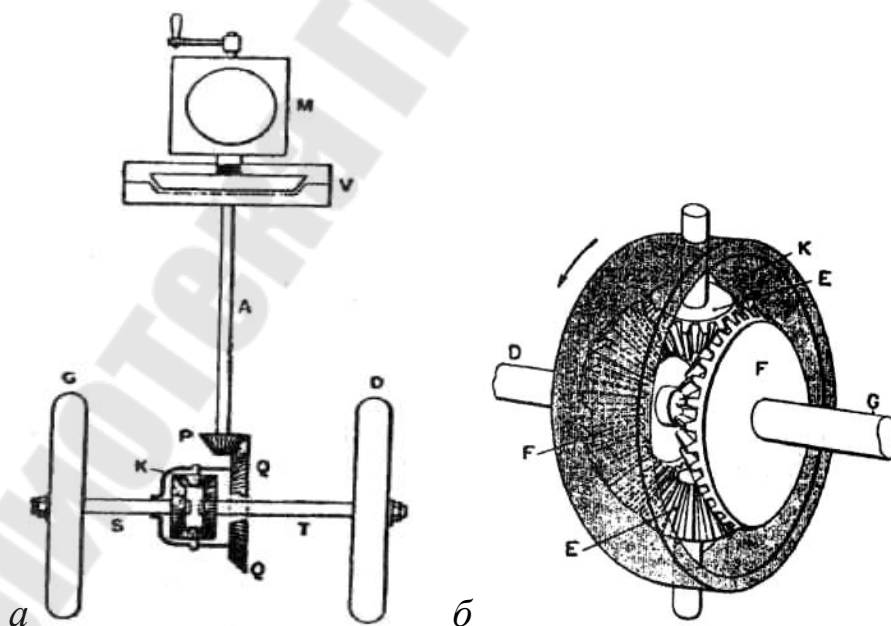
Схема привода колес (а), эскиз дифференциала(б).
